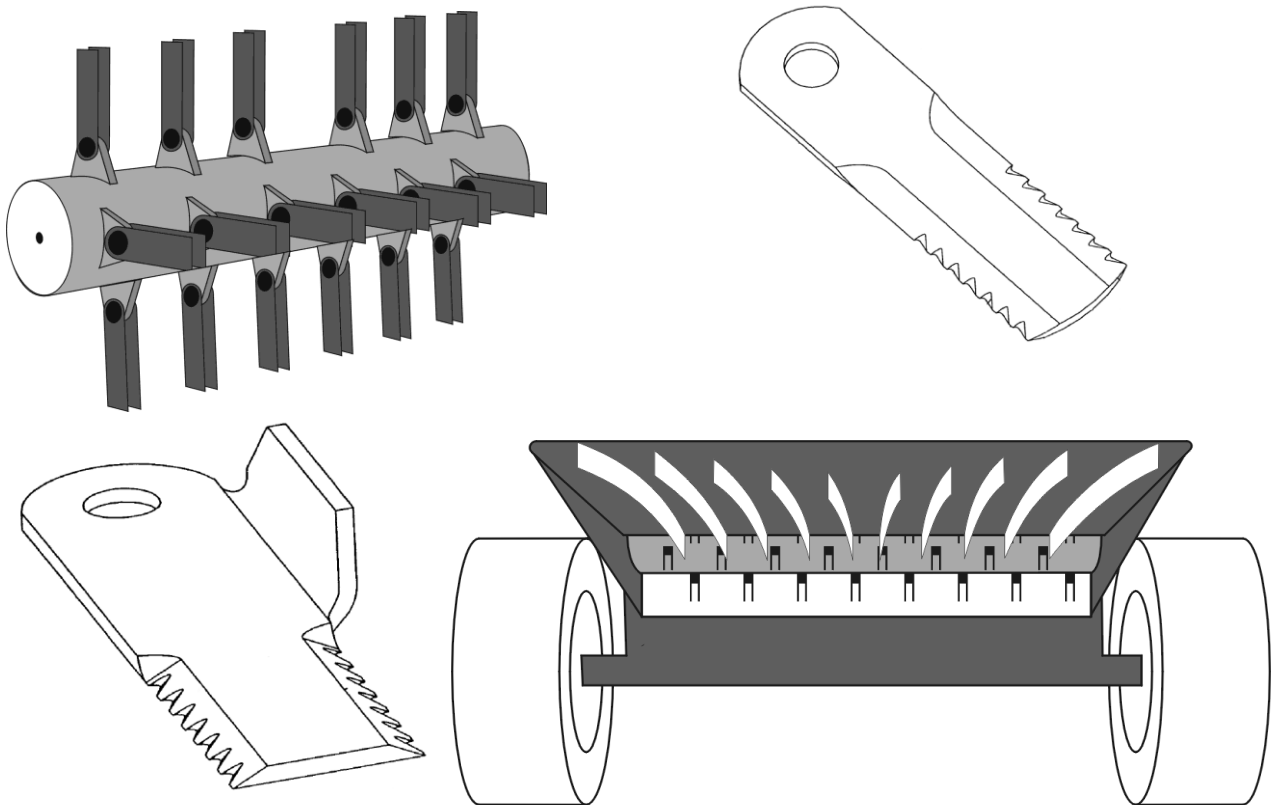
vista posterior de un cilindro picador y cubierta con guías para distribuir los residuos de cosecha.
